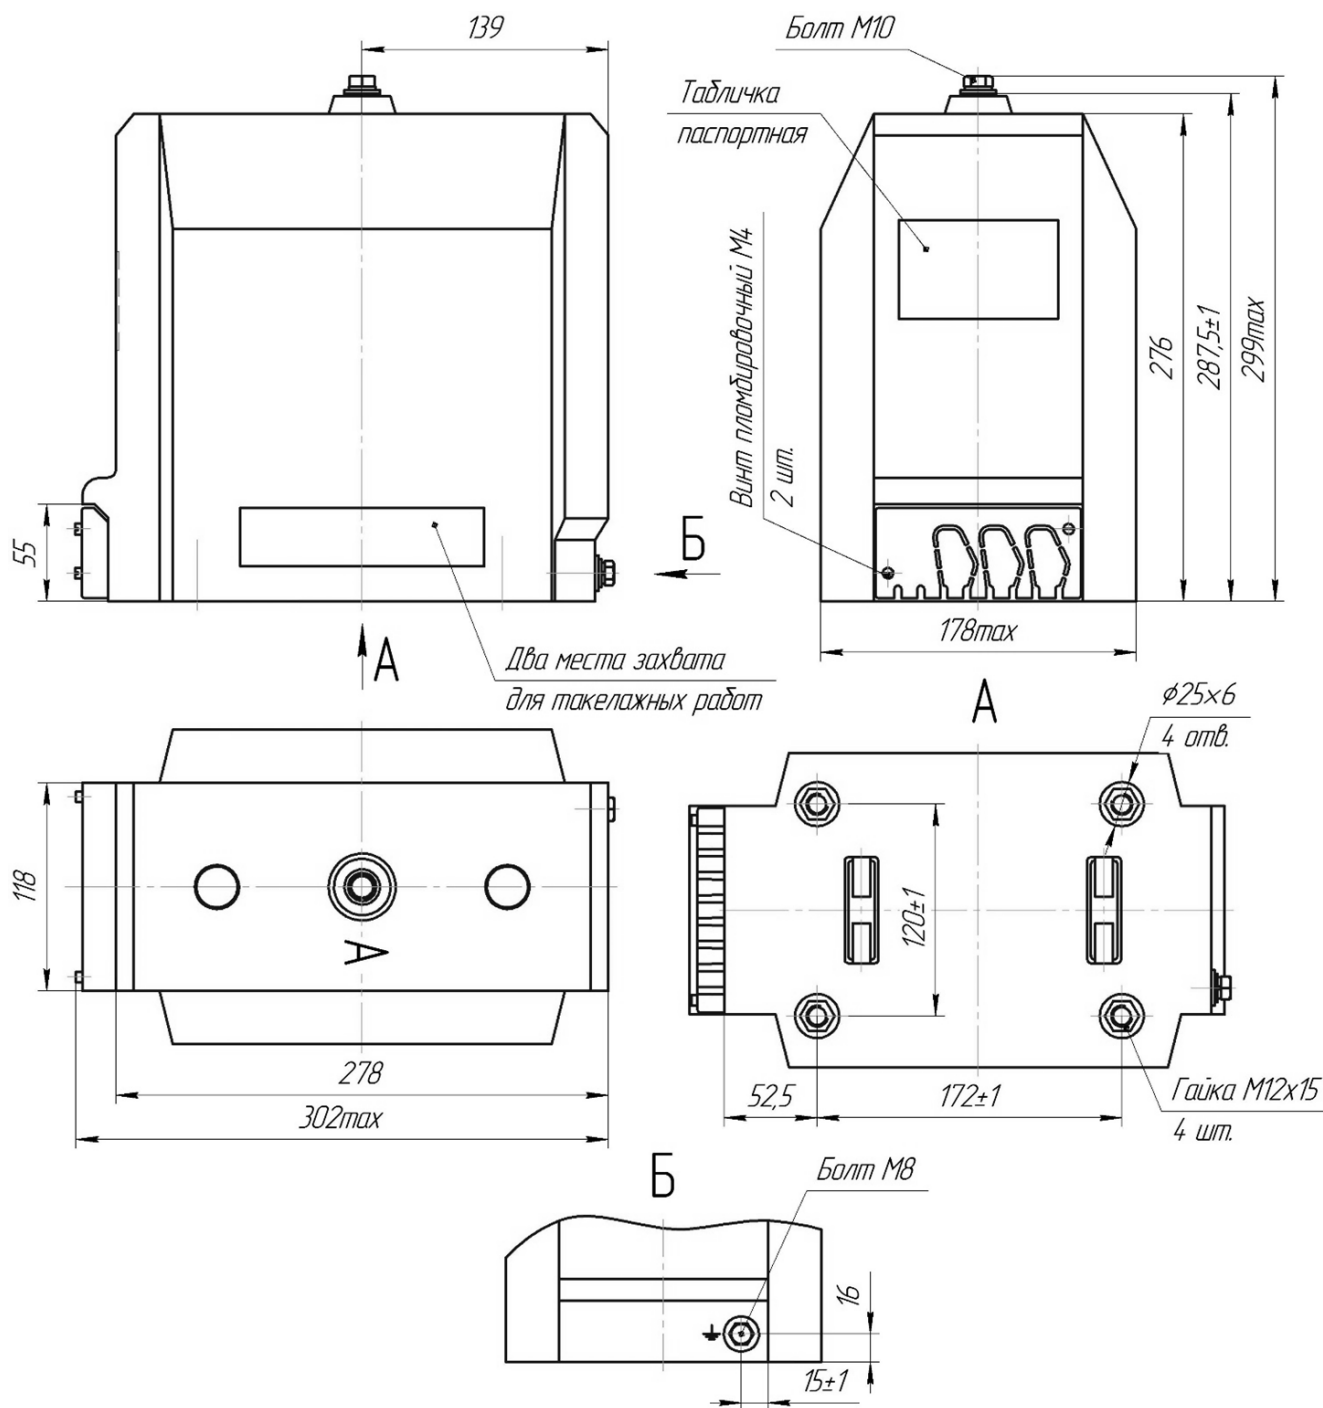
Габаритные, установочные и присоединительные размеры трансформаторов напряжения ЗНОЛ-СЭЦ-15-10 и ЗНОЛ-СЭЦ-20-10
